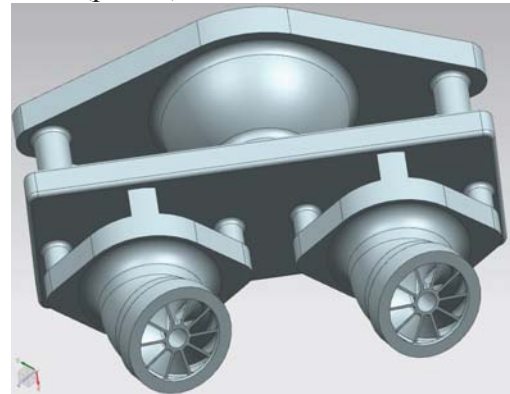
3D-модель заготовки с литниково-питающей системой
